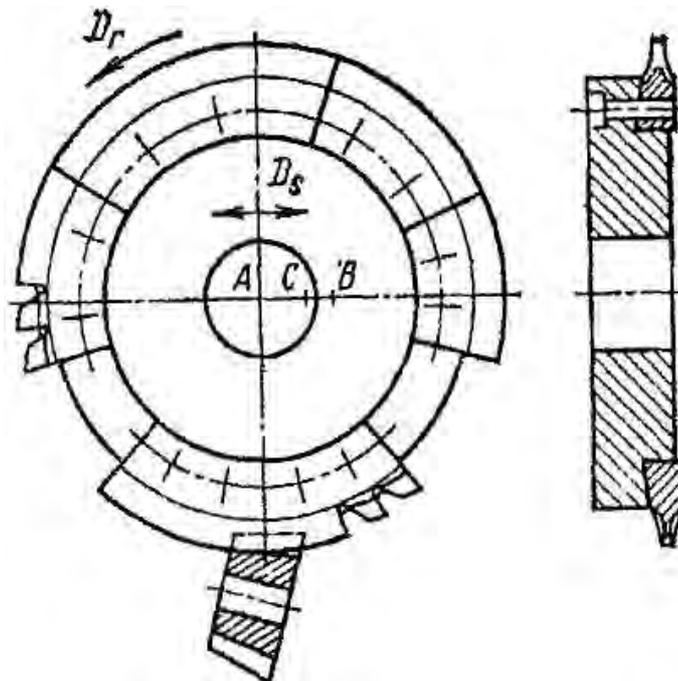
Схема обработки конического прямозубого колеса фрезой-протяжкой
